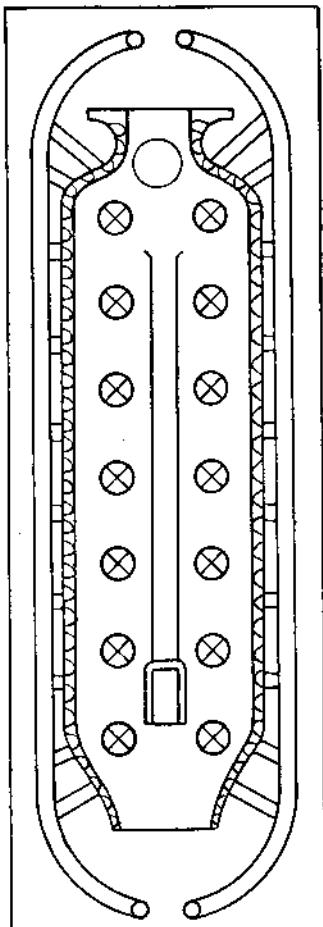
Схема формовки верхнего картера фланцем вверх, ползов металла рожками вниз.
